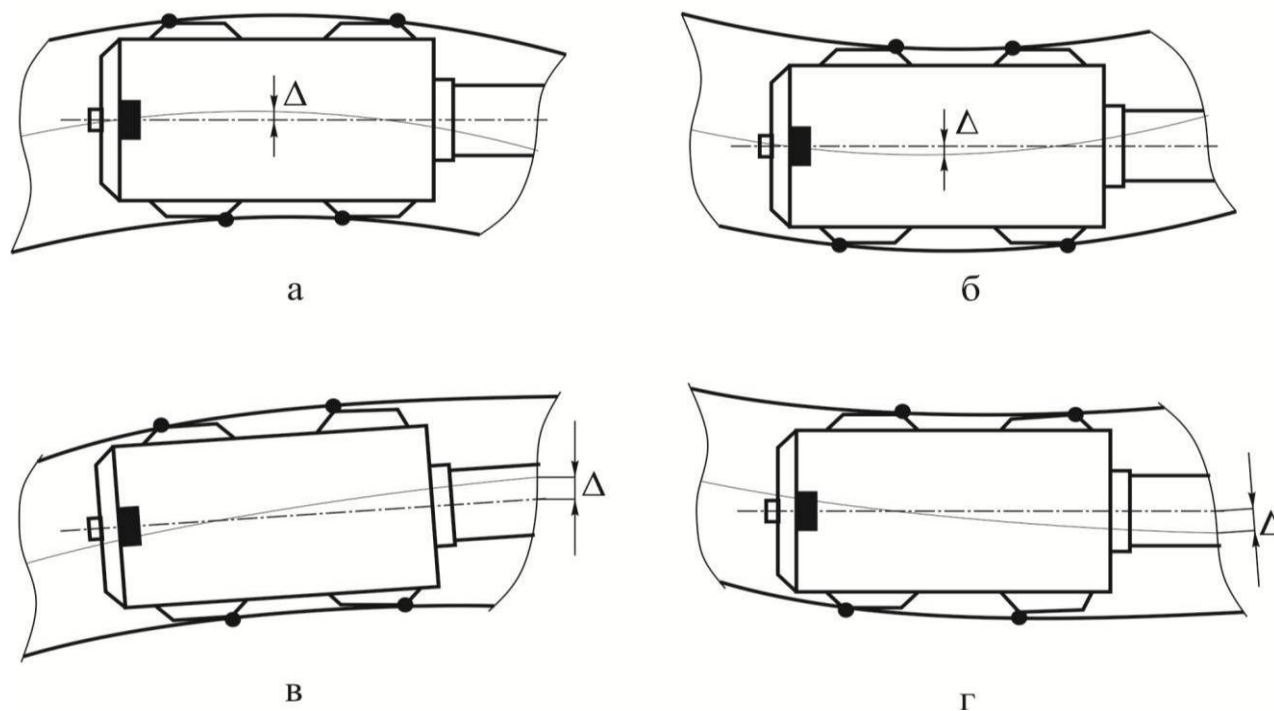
Точки контакту напрямних шпонок з поверхнею заготовки
